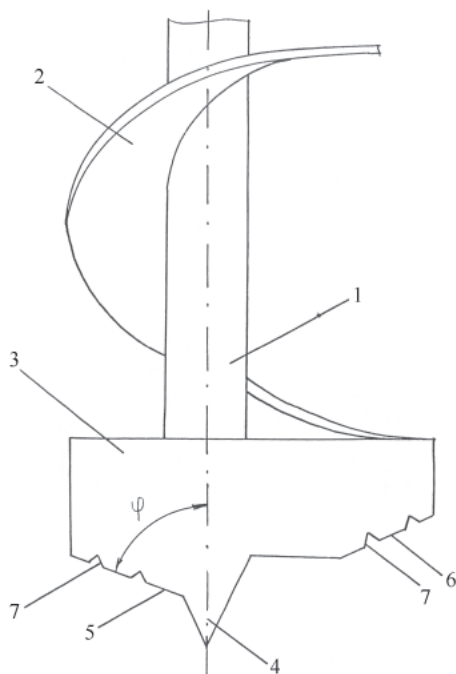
Сверло с режущей частью для разработки сквозного шурфа в древесине пня: 1 – стержень; 2 – шнек; 3 – рабочая часть; 4 – направляющий центр; 5 – меньшая режущая кромка; 6 – большая режущая кромка; 7 – двухгранные канавки
